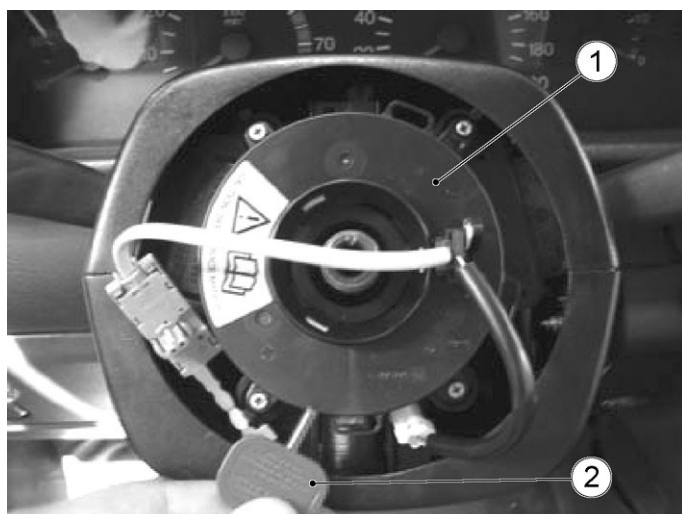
Установка нового соединителя с устройством вращающимся:
